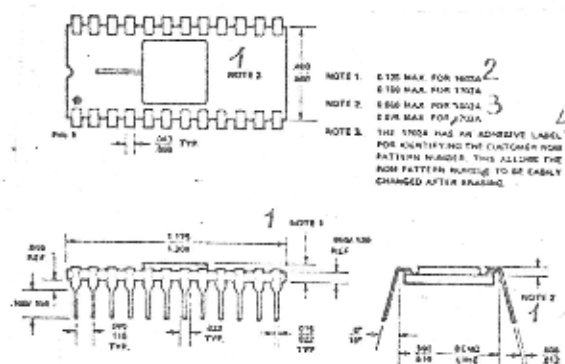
Схема 24-штырькового керамического корпуса с двухсторонним расположением выводов/S/:
